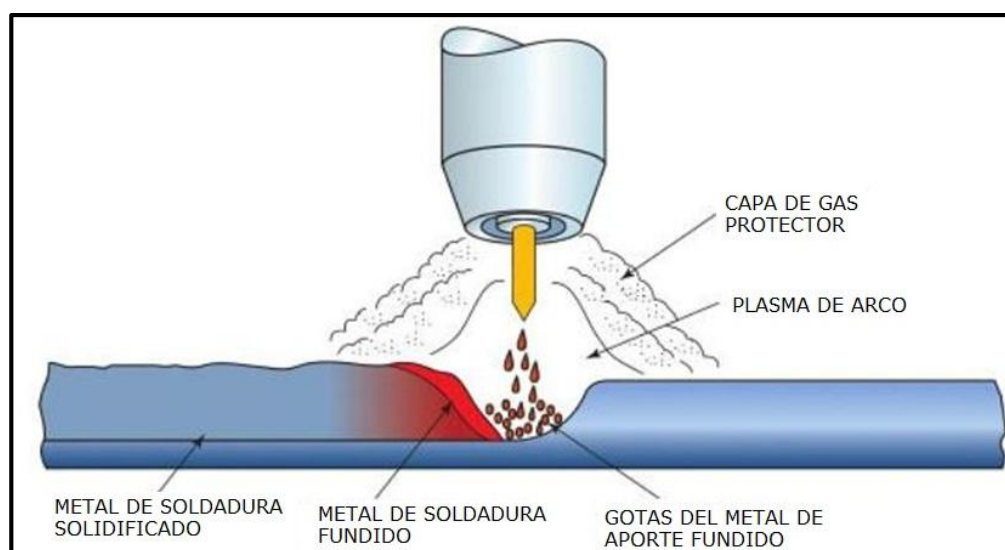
Proceso de soldadura por arco GMAW (15).
